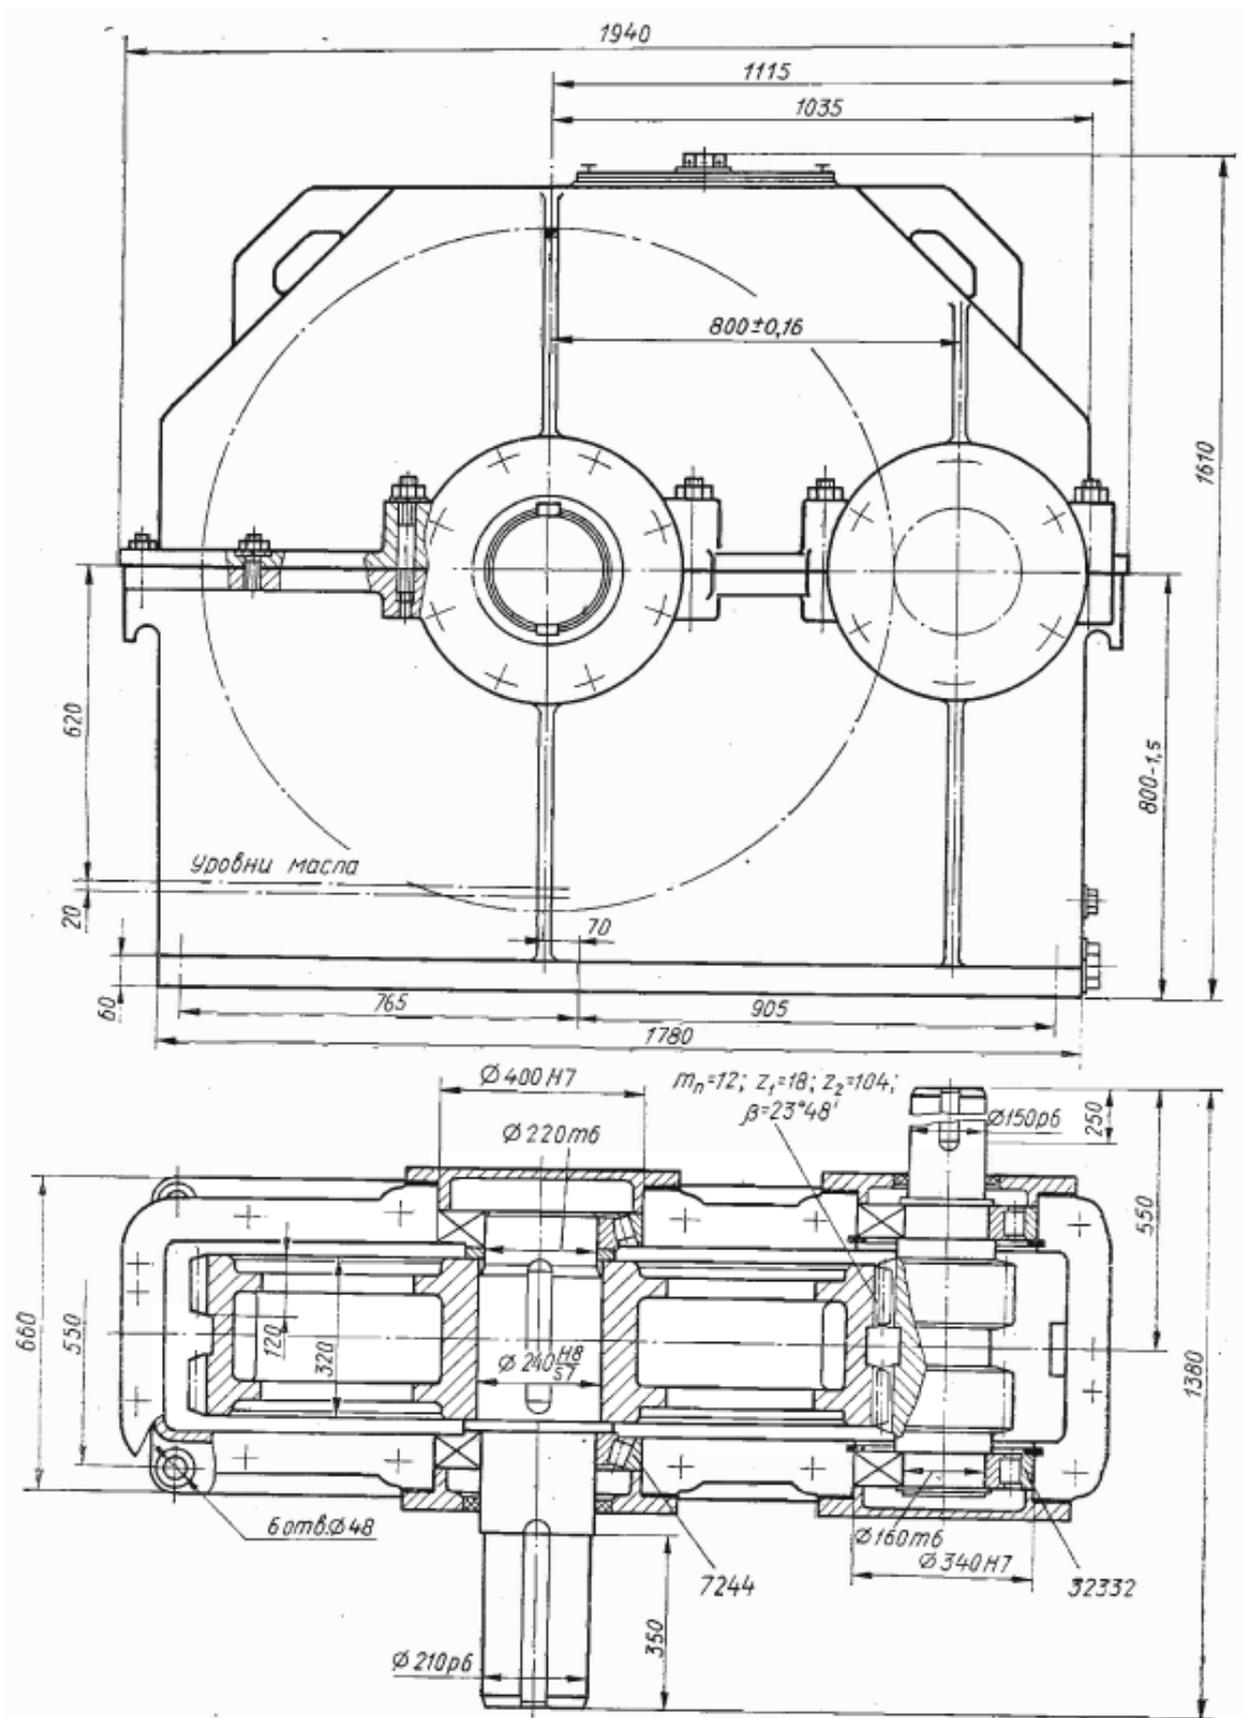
Редуктор с шевронной передачей и плавающим быстроходным валом
